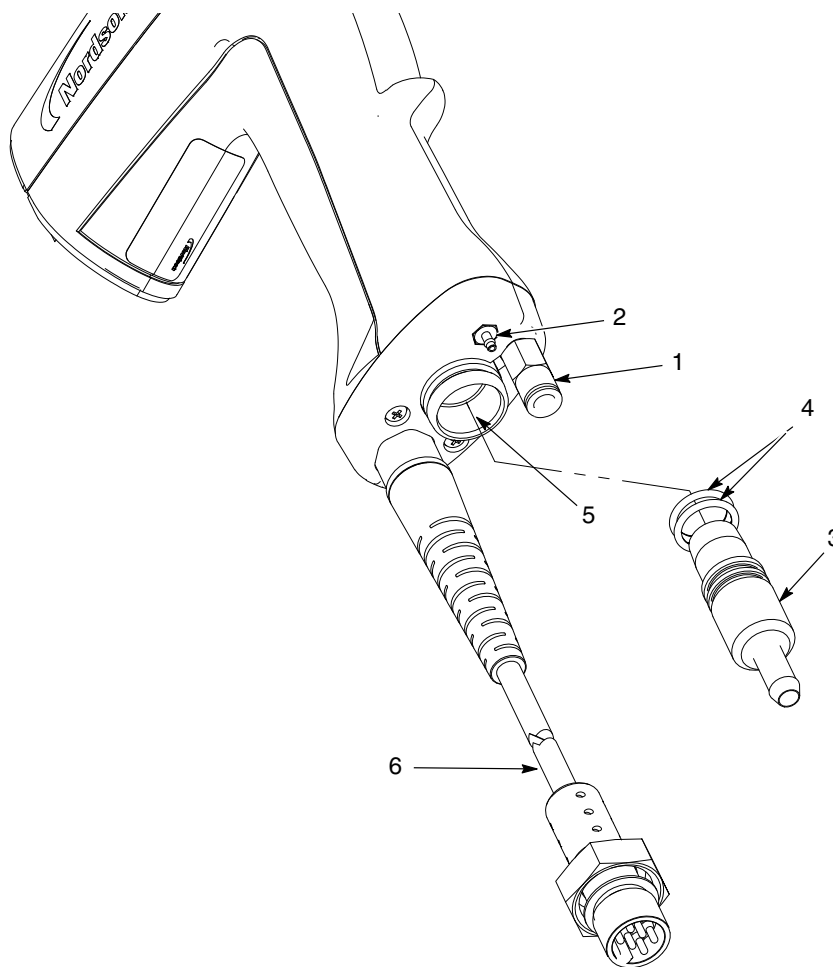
Připojení přívodu vzduchu do systému a do pistolí
